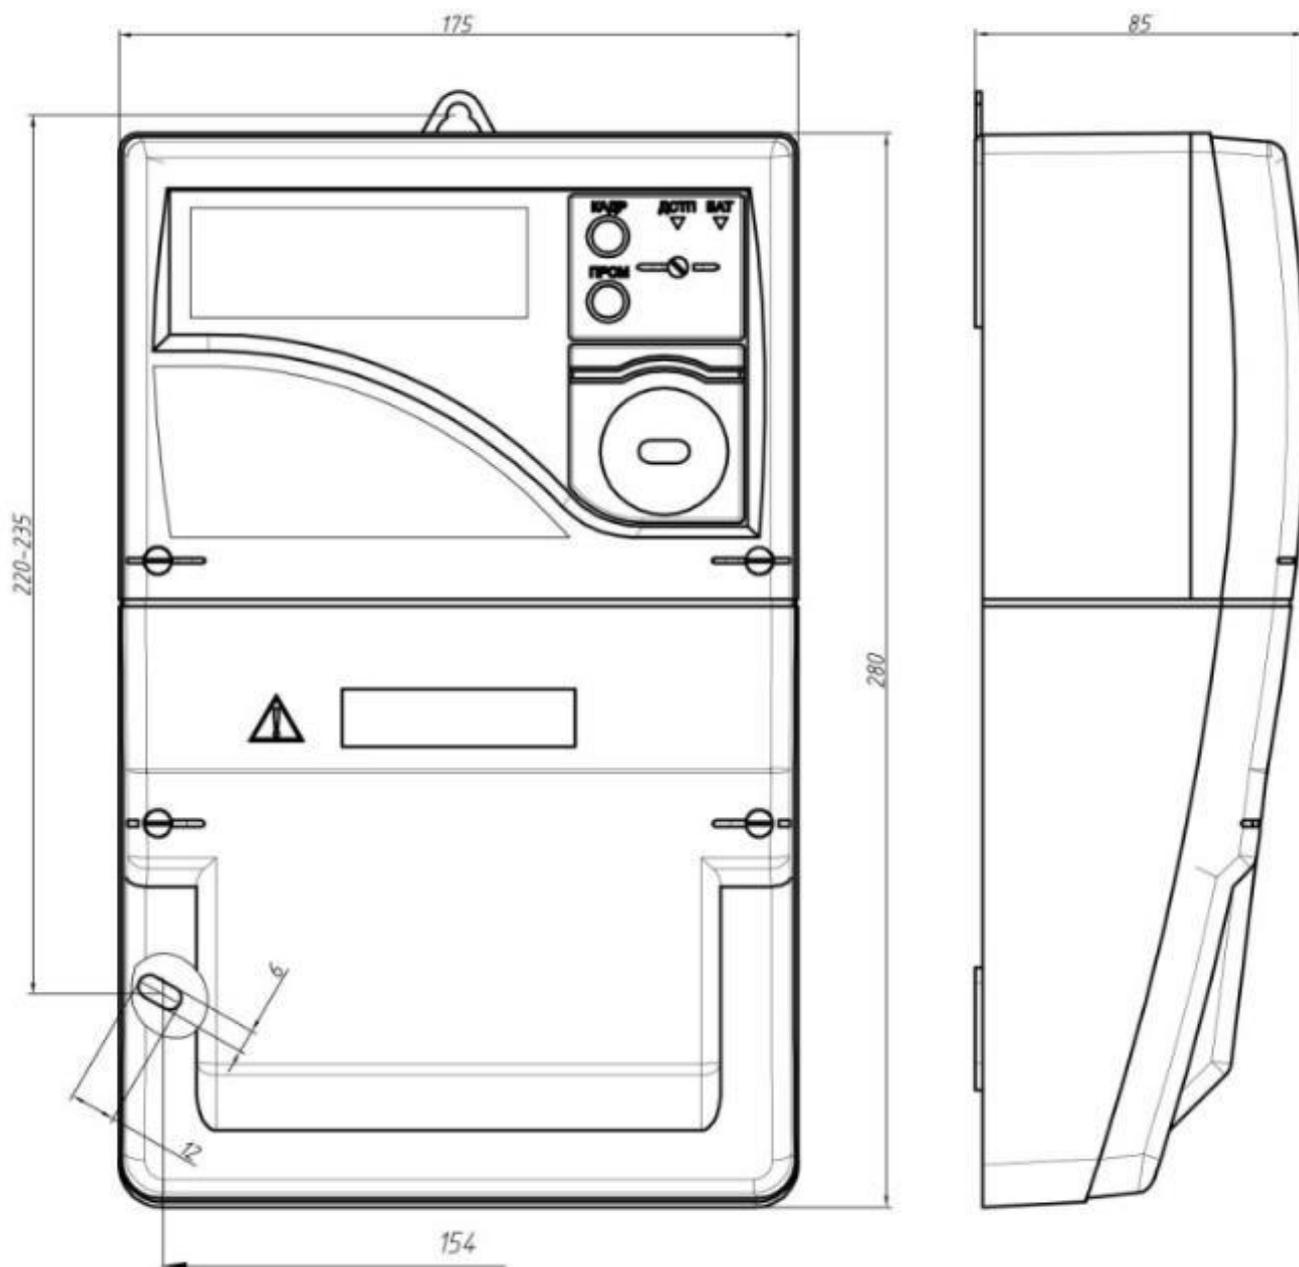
Габаритные размеры счетчика в корпусе «S34»
